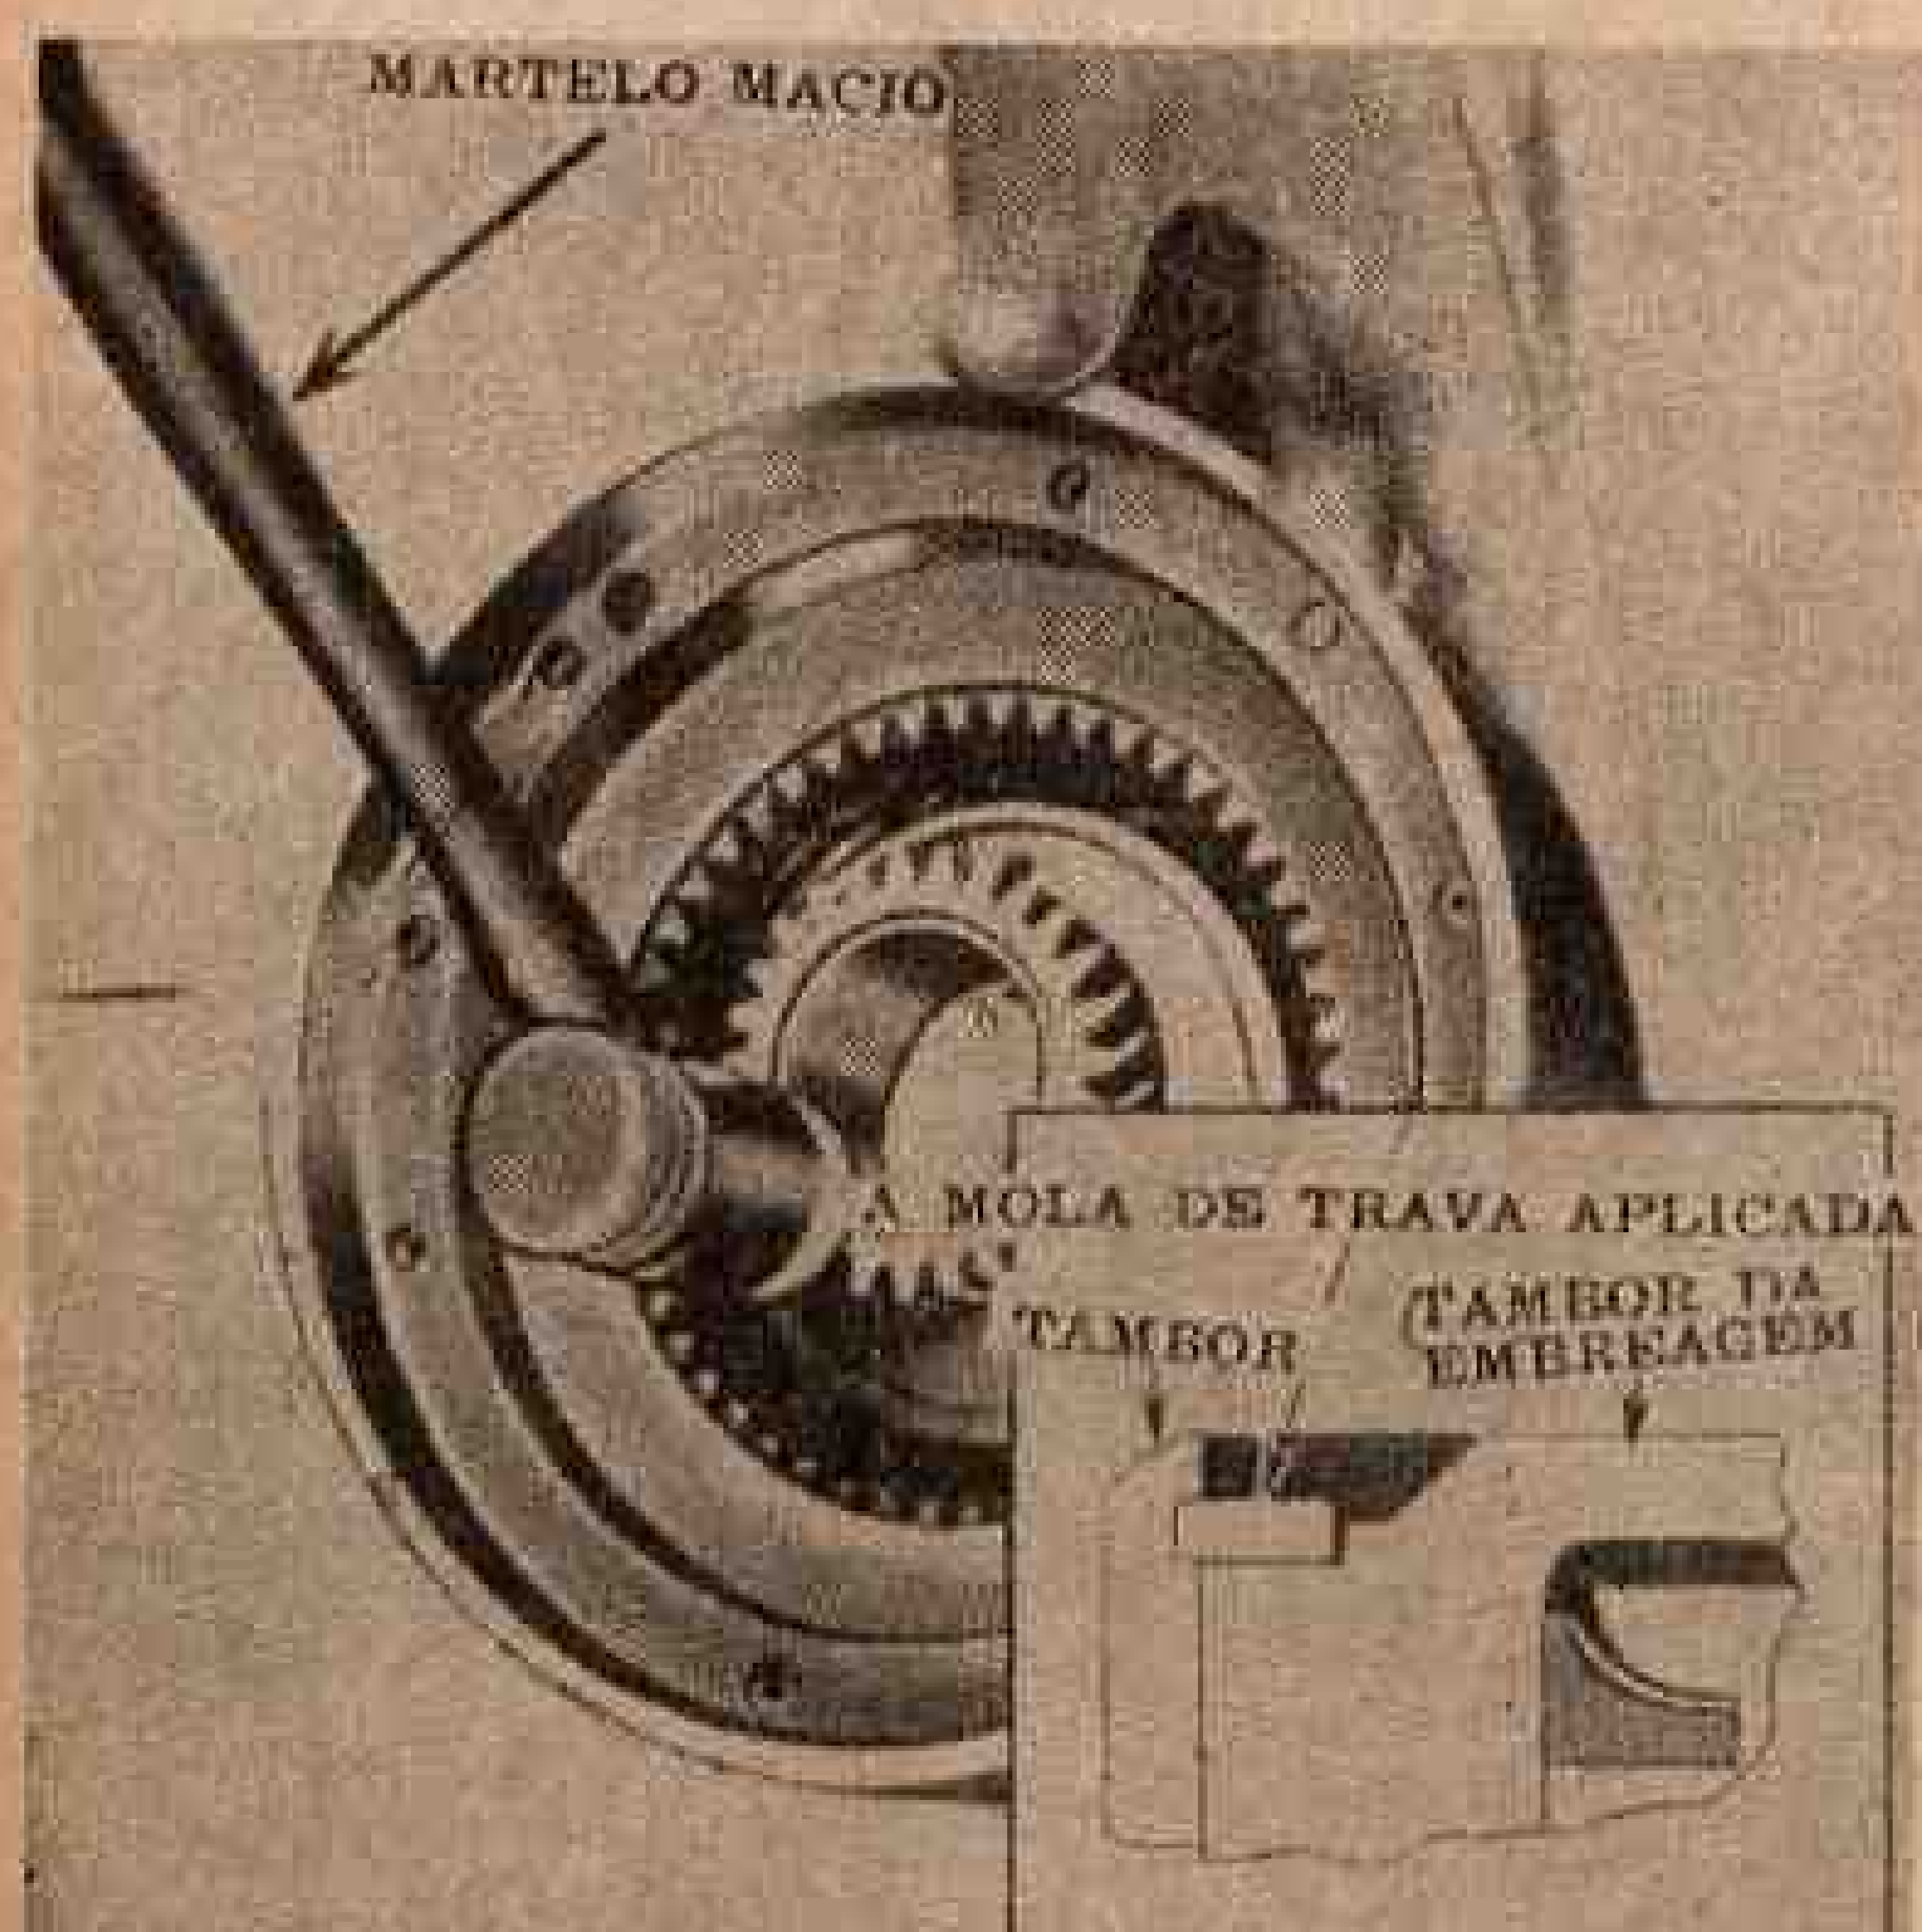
Assentando o tambor da embreagem contra o anel de trava.
